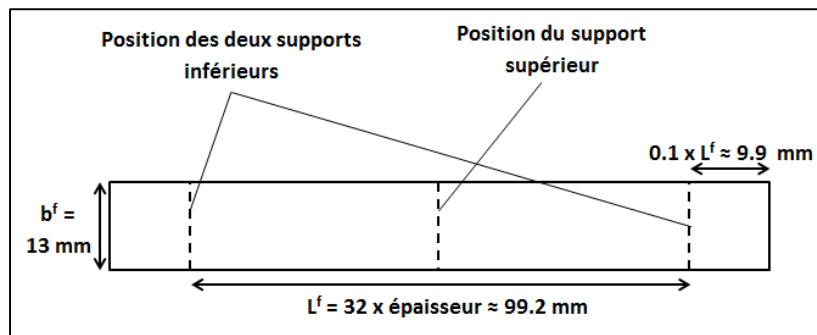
Géométrie de l'éprouvette de flexion trois points (tirée de ASTM D7264)
